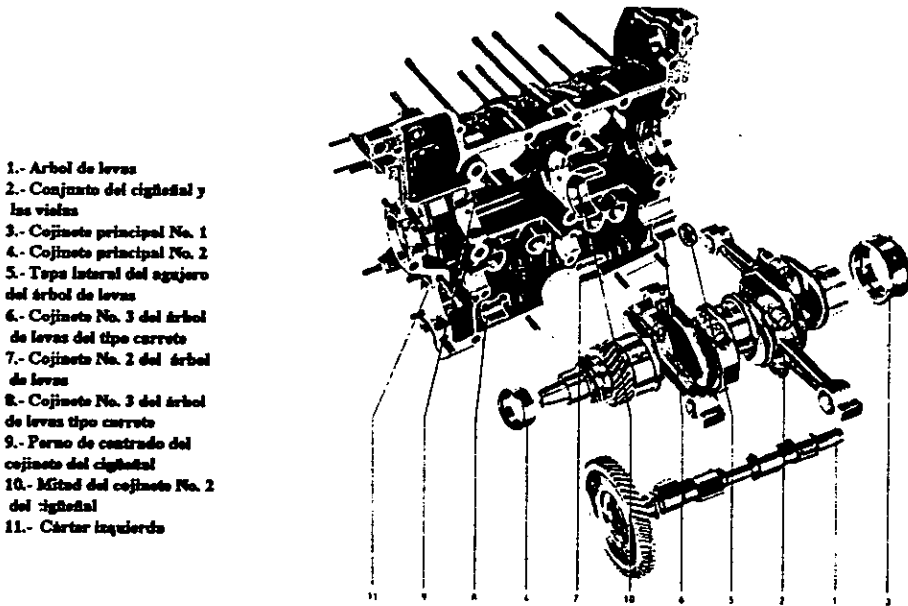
Vista esquemática de medio conjunto del cárter.
